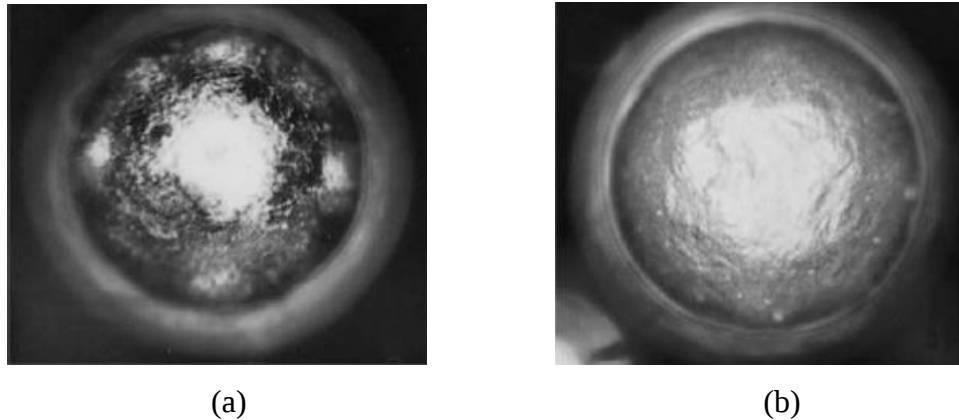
Bolas de soldadura 62Sn/36Pb/2Ag: (a) bola brillante, (b) bola opaca [2].
